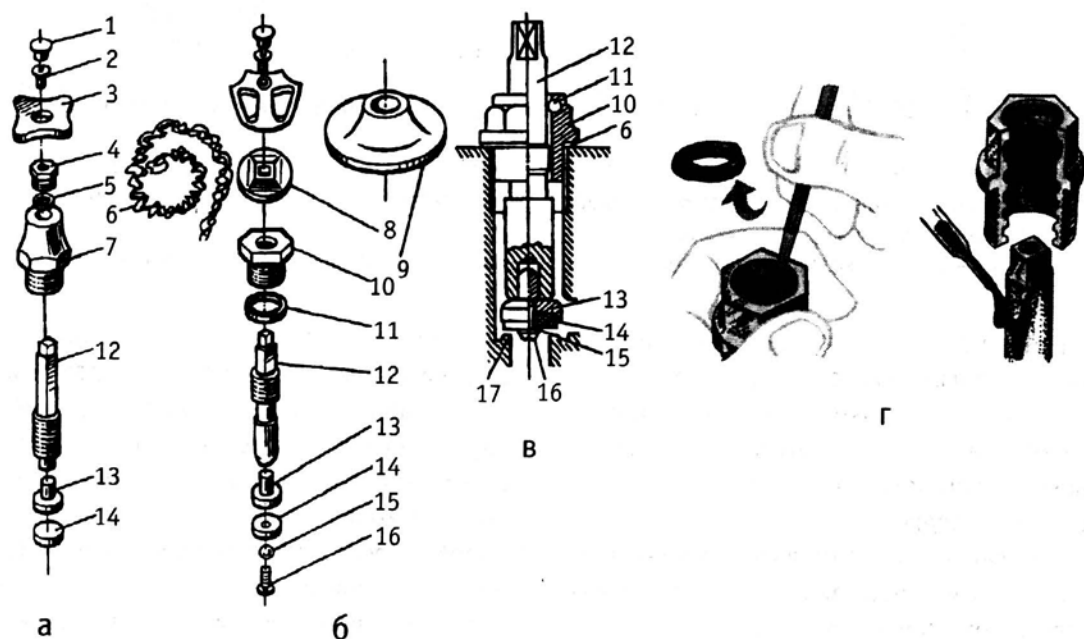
Вентильные головки с удлиненным штоком: а — деталировка вентильной головки с хромированным корпусом; б — деталировка вентильной головки с резиновым кольцом; в — вентильная головка в сборе; г — замена резинового сальника;
